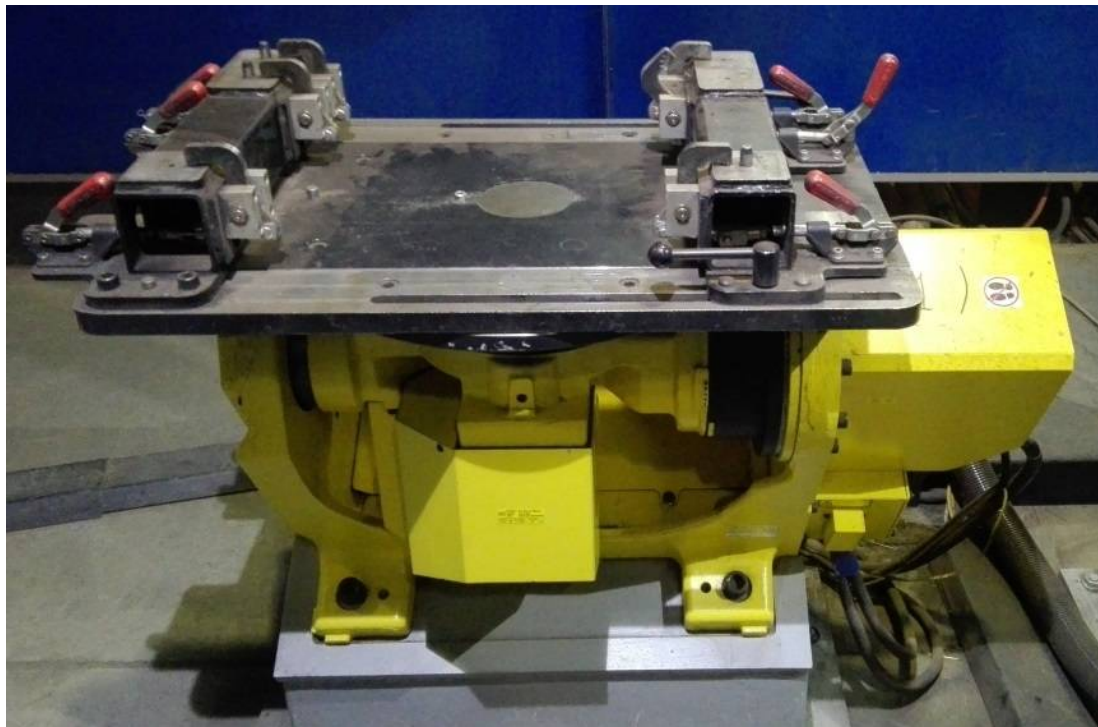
Двухосевой позиционер FANUC и приспособление для установки котла
